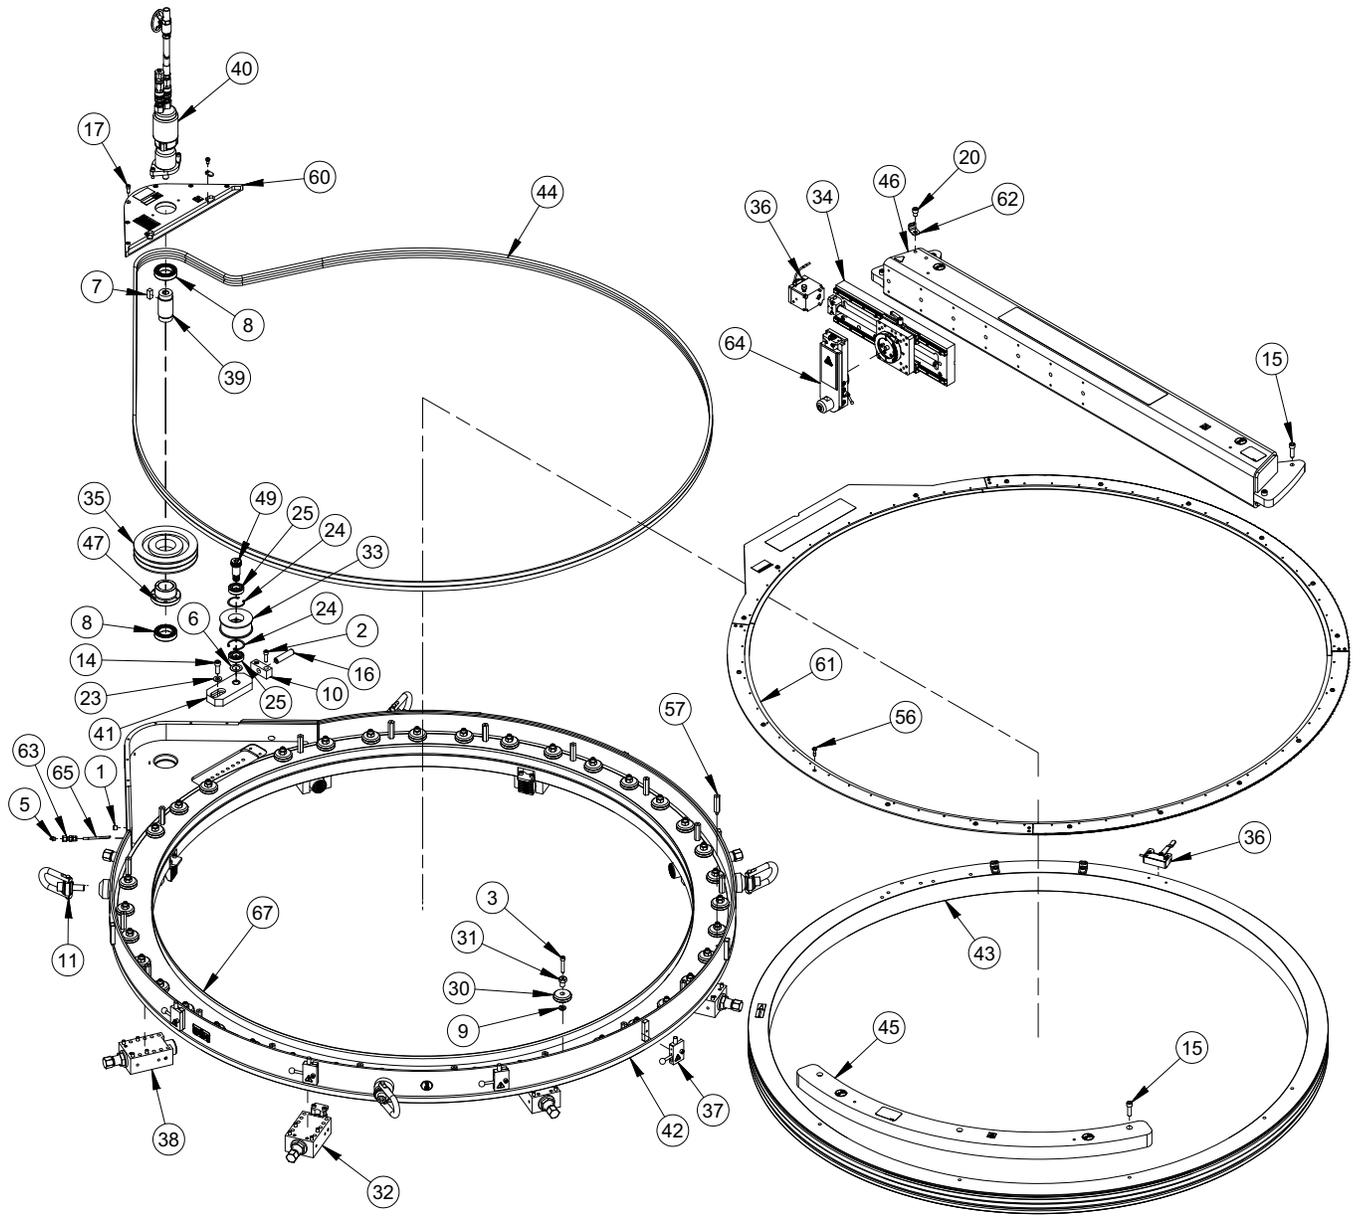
ENSEMBLE ODF70 SPEED FACER (RÉF. 87000)
